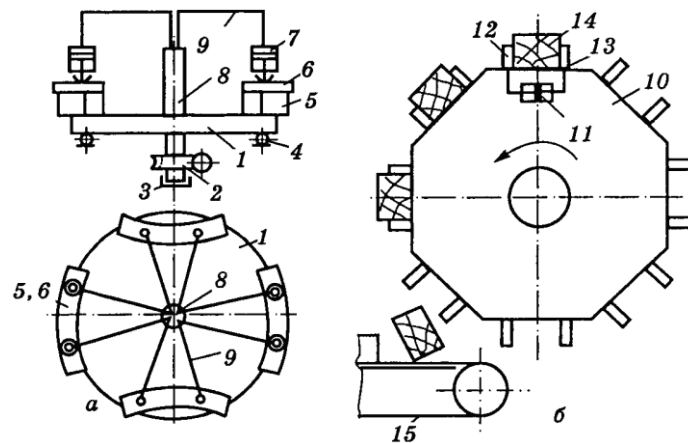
Схеми механізмів подачі: *а* – карусельних; *б* – барабанних: 1 – карусельний стіл; 2 – черв'ячна передача; 3 – п'ята; 4 – круговий кульковий підшипник; 5 – шаблон; 6 – заготівка; 7 – пневмоциліндр; 8 – повітророзподільник; 9 – трубопроводи; 10 – барабан; 11 – пневмоциліндр; 12 – рухомий упор; 13 – нерухомий упор; 14 – заготівка; 15 – транспортер
